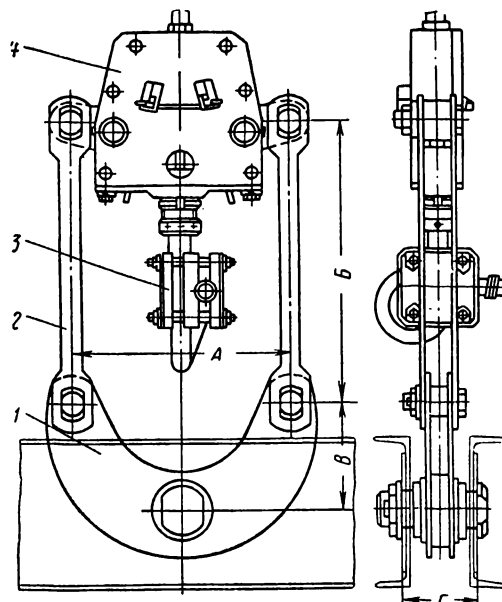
Подвесное устройство с коушем типа КРГ для скипов:
